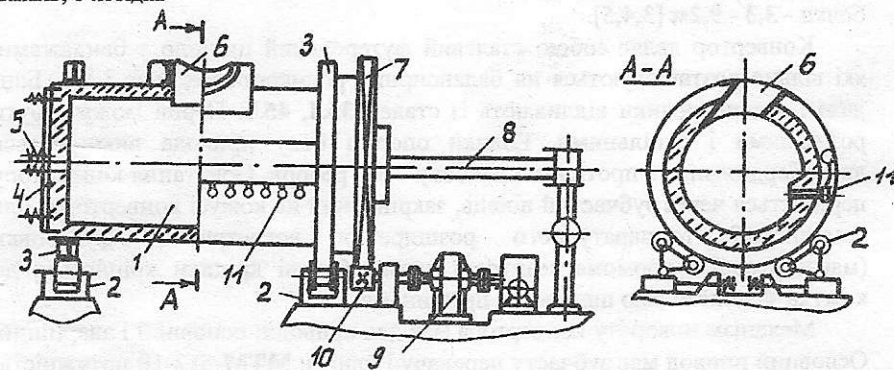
Схема горизонтального конвертора: 1-бочка; 2-балансирні роликоопори; 3-бандаж; 4-бокова кришка; 5-підпружинена шпилька; 6-горловина; 7-зубчастий вінець; 8-грубопровід; 9-привод; 10-приводна шестерня; 11-фурми
